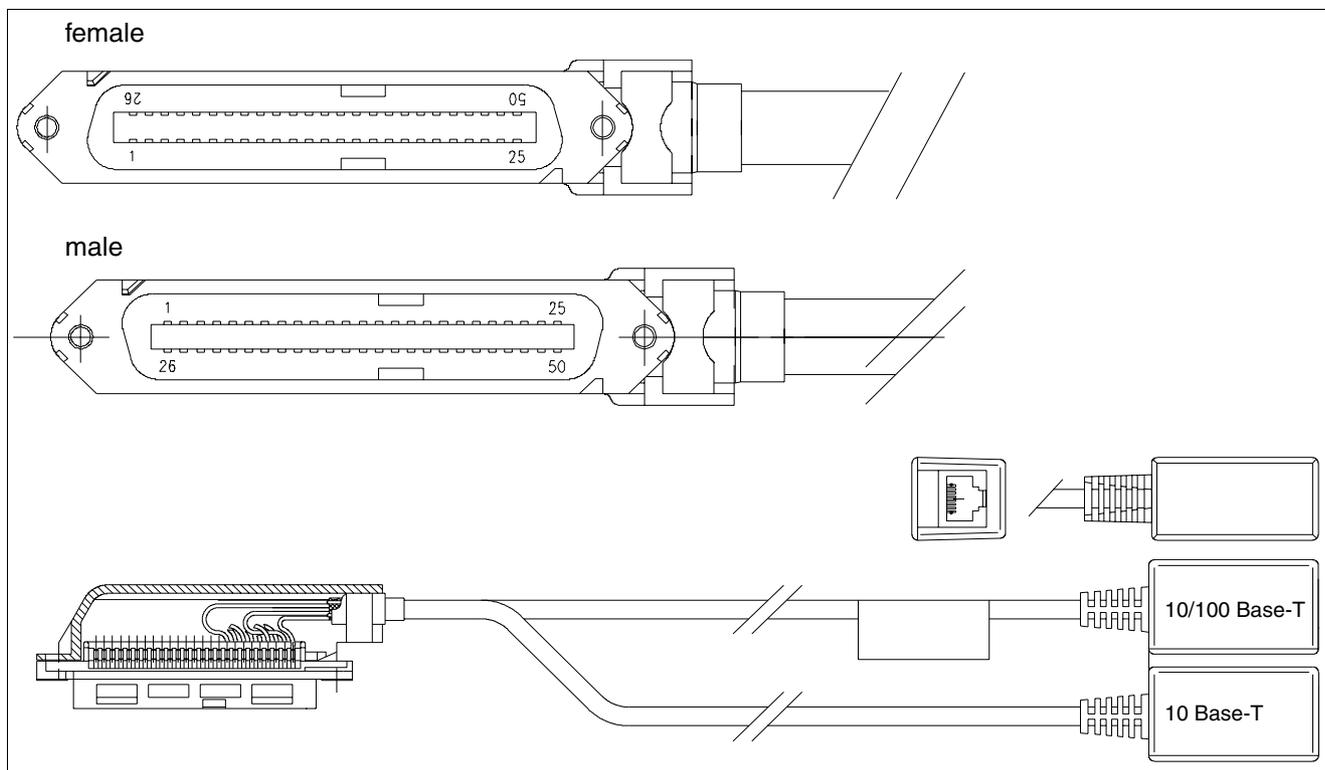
LAN Adapterkabel (mit Stecker female bzw. male – nur für USA)
